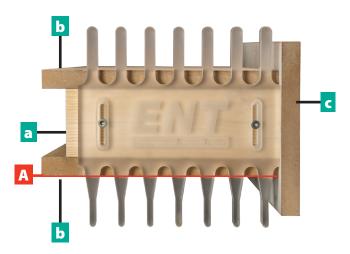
Montage der Holzteile für die Aufnahme und Befestigung der Schablone
